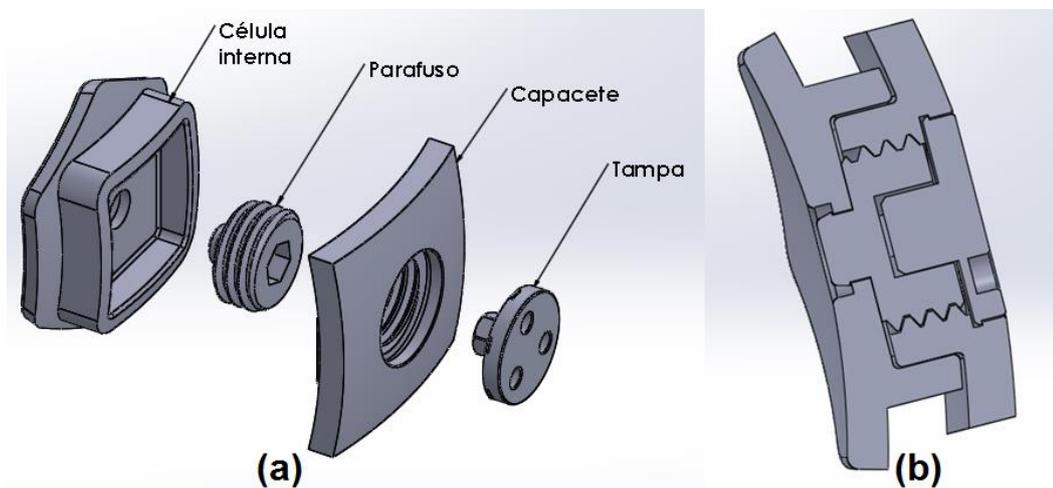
Segundo mecanismo de ajuste (a) explodido e (b) com vista em corte.
